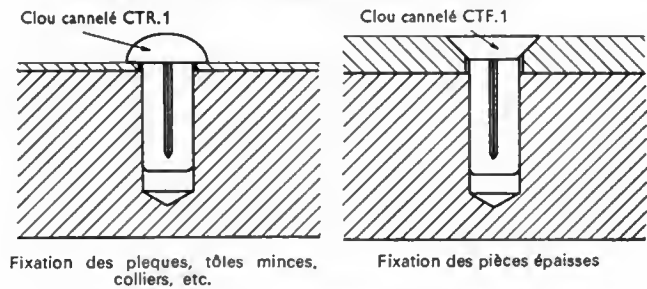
Assemblages per clous cannelés L.G.C.
